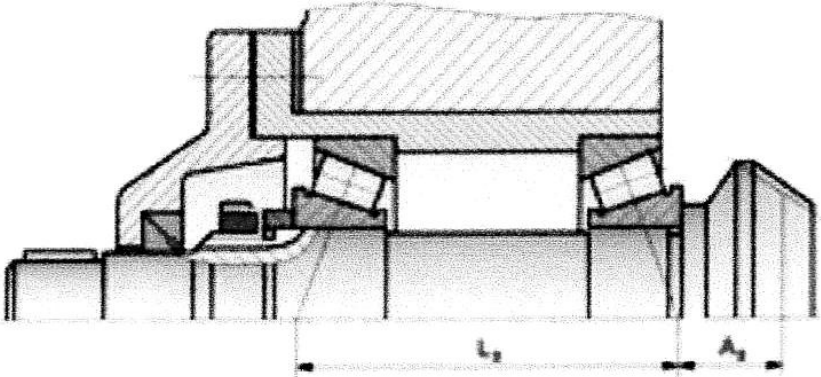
Конструкция вала с установкой подшипников «в растяжку».
